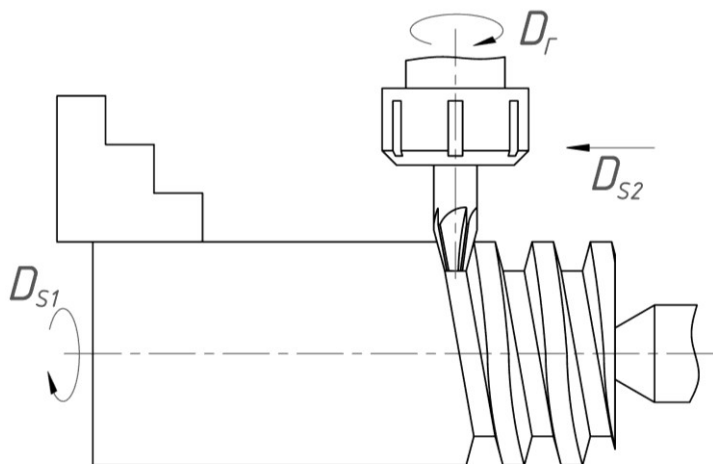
Фрезерование трапецеидальной резьбы концевой фрезой.
